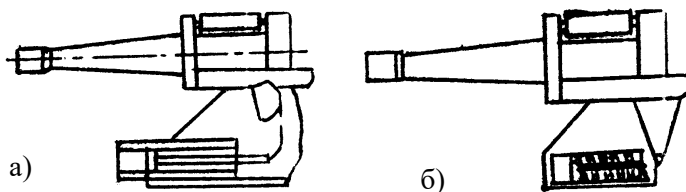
Схеми розміщення зрівноважувальних механізмів:
